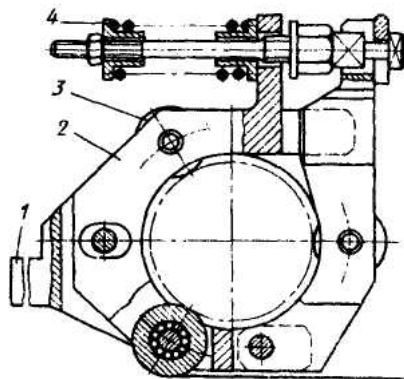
Трироликів пристрій для обкатування нежорстких валів: 1 – корпус; 2 – плаваючий тримач; 3 – ролик; 4 - пружина
